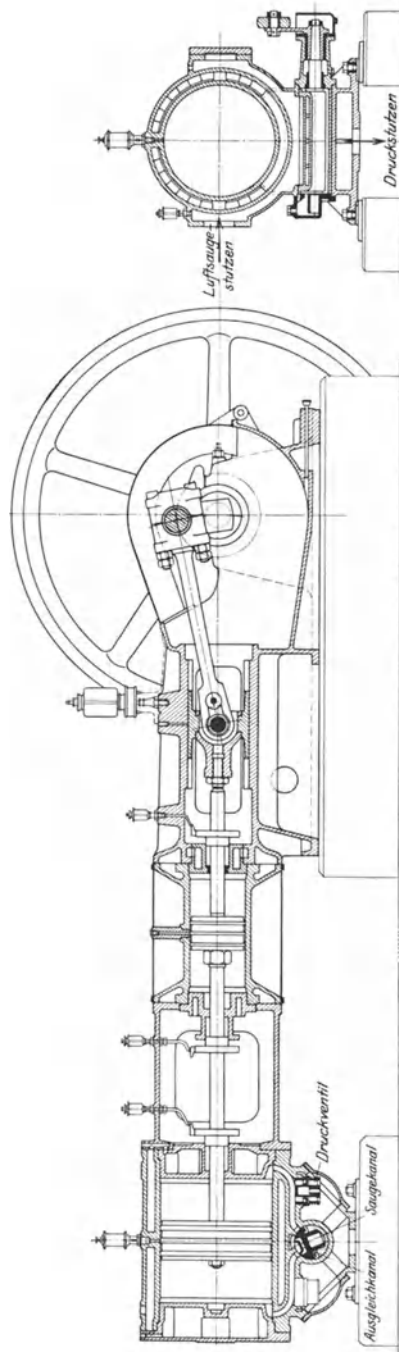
und 220. Dampfgetriebene einstufige Kolbenluftpumpe mit Druckausgleich der Maschinenbau-A.-G. Balcke.
